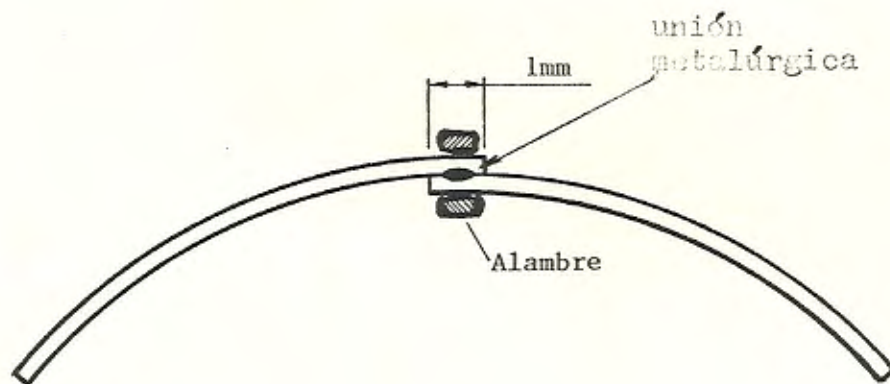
Ancho de solapa de soldadura Soudronic Automática.
